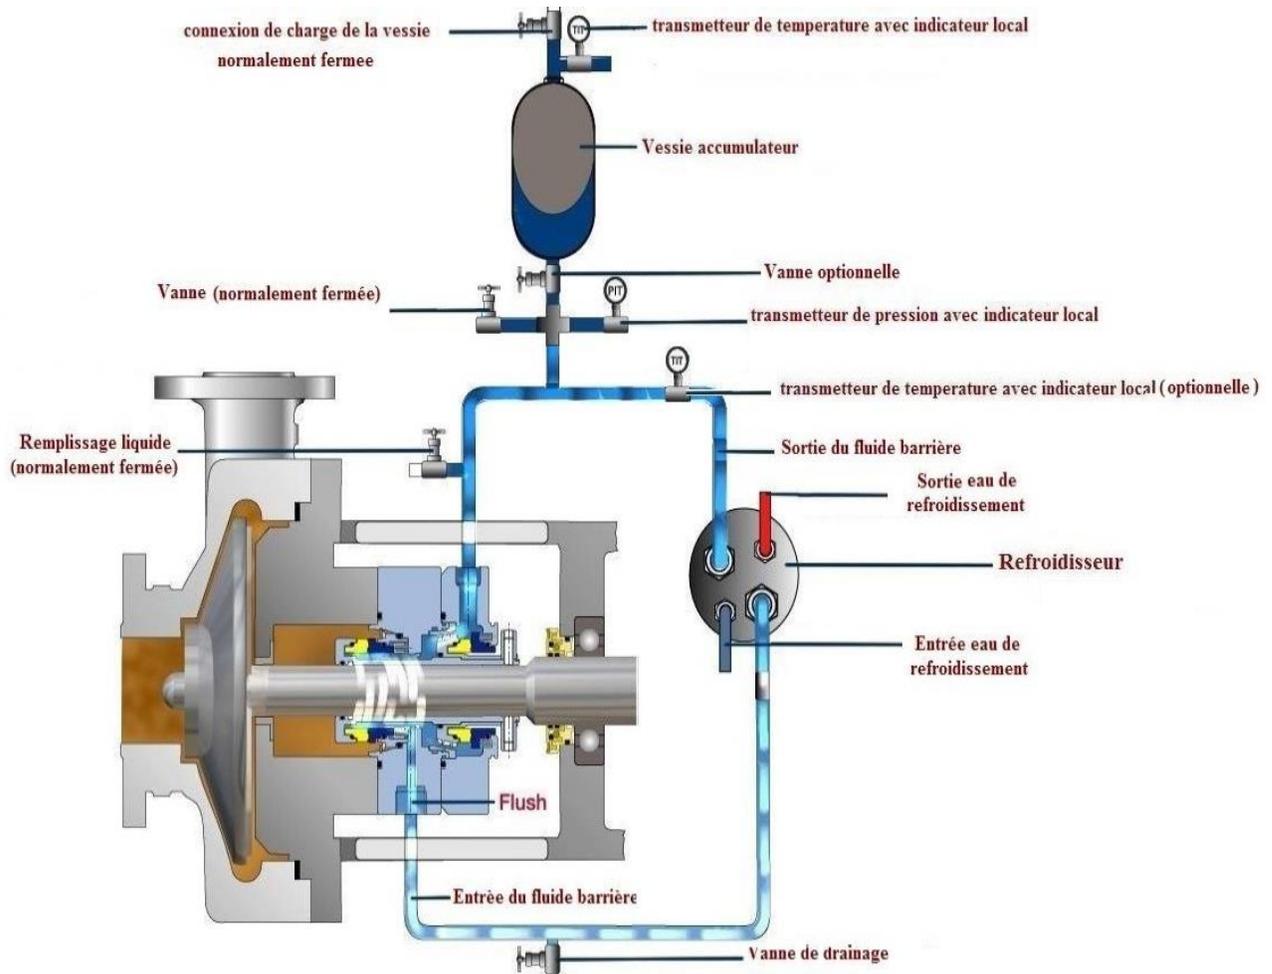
Schéma détaillé d'une pompe API Plan 53B
